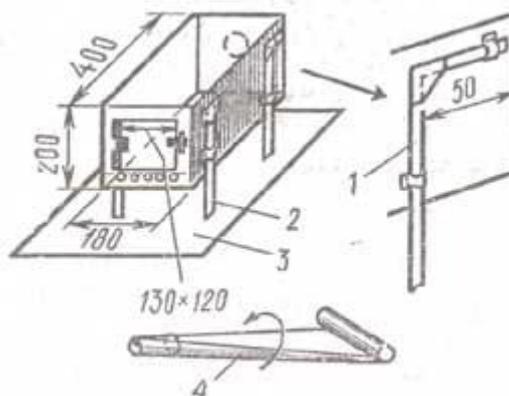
Прямоугольная печь (1, 2 — поворачивающаяся ножка; 3 — подставка; 4 — сворачиваемая труба)
